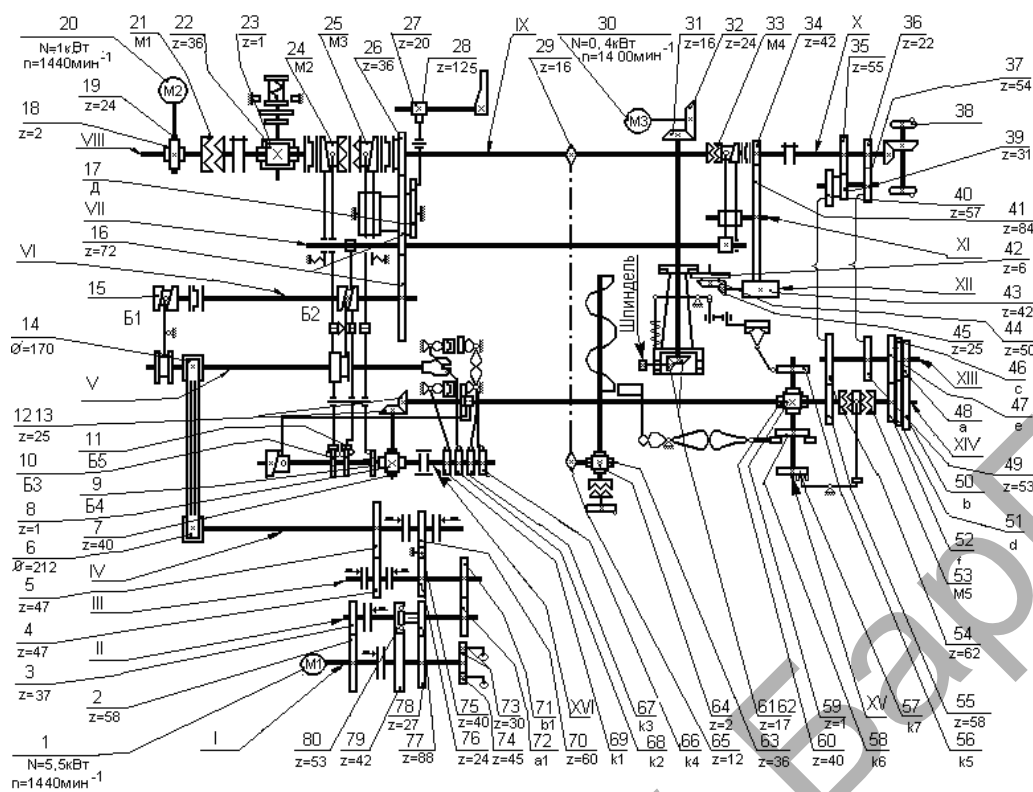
Кинематическая схема токарно-револьверного автомата модели 1E140П
